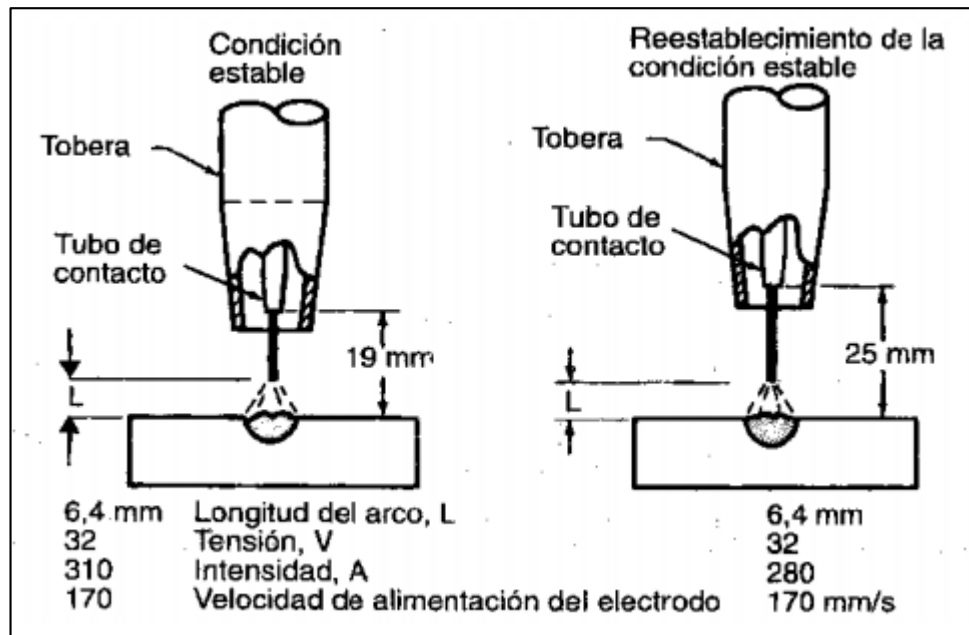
Autorregulación del arco en el proceso de soldadura GMAW
